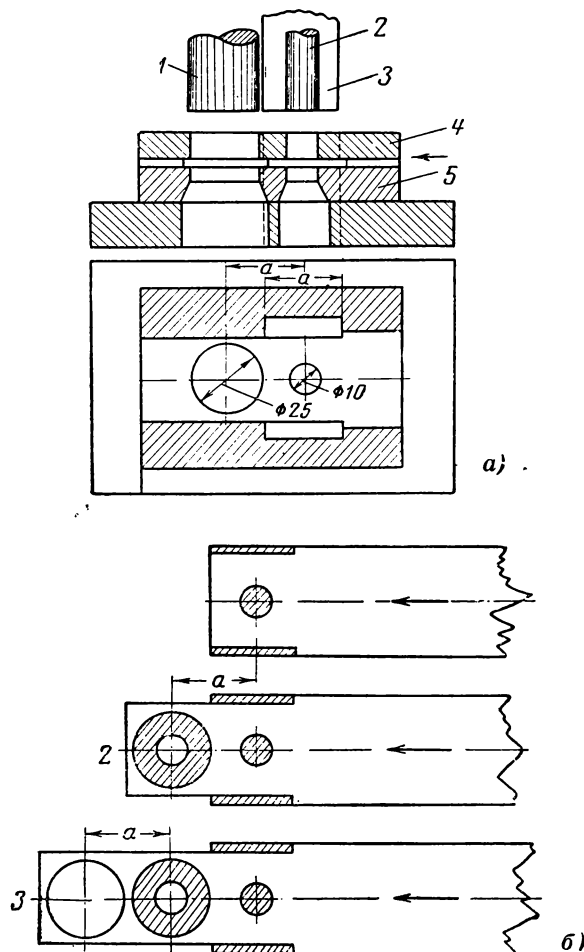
Последовательный штамп для шайбы. а — устройство штампа; б — схема штамповки.
